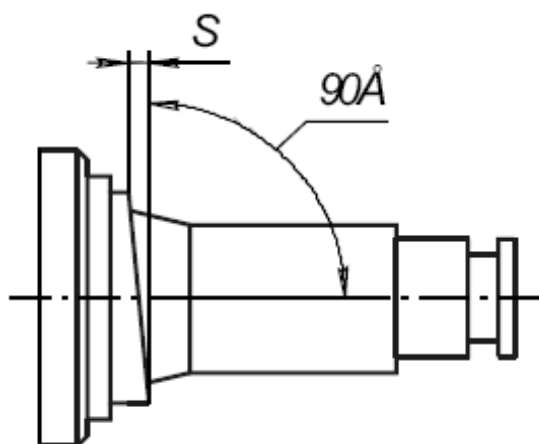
Схема измерения величины торцевого биения заплечика валка.
